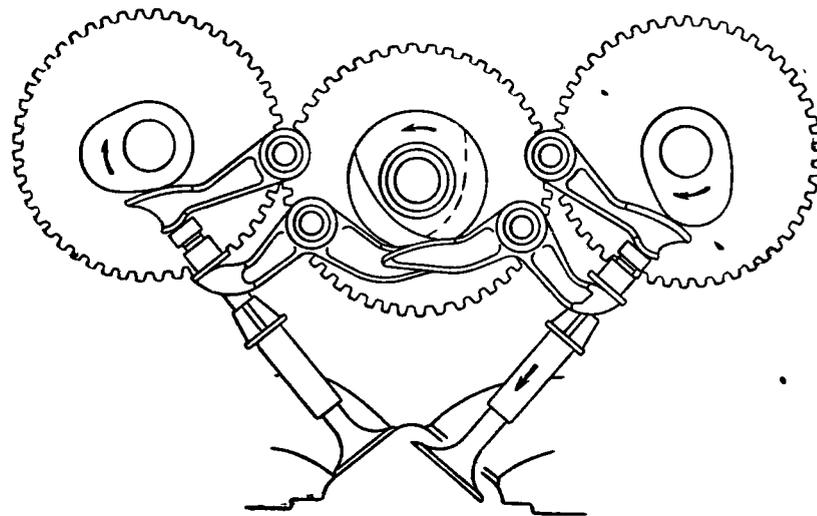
Схема распределительного механизма двигателя Дукати (десмодромик).
